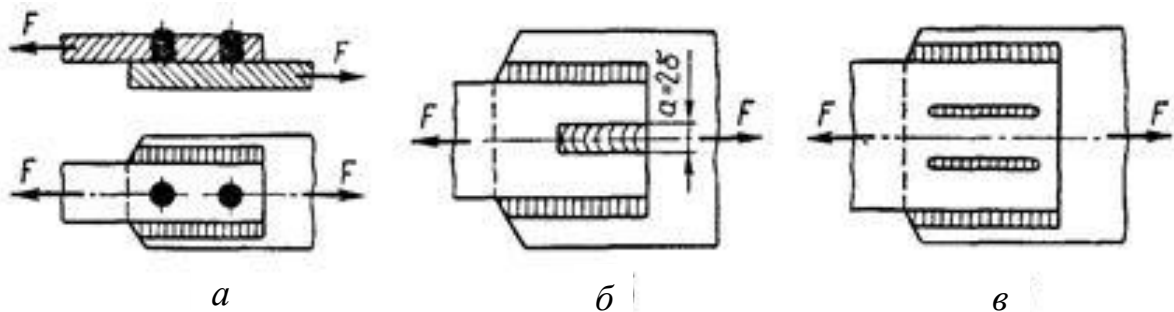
Схема зварного напусткового з'єднання з несиметричним розміщенням флангових швів
